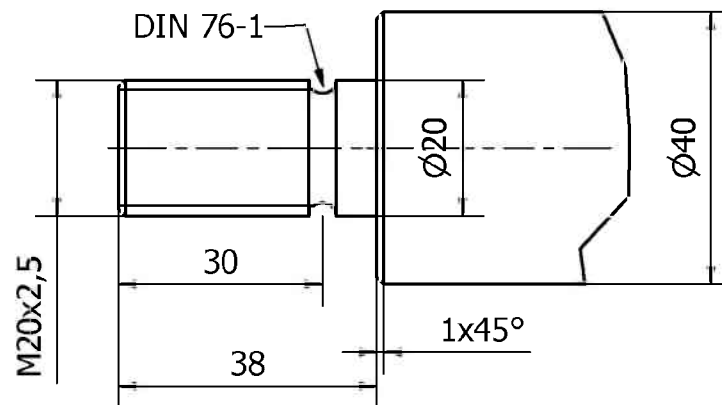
Gewindedetail der Führungssäule: Die Verschraubung erfolgt über ein M20 Außengewinde mit einem Gewindegang laut DIN76 – 1 [24].
